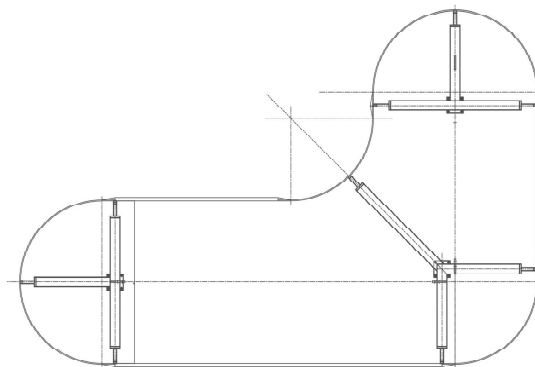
Neue Seilführung, -spannvorrichtung und -befestigung [Woh20]
